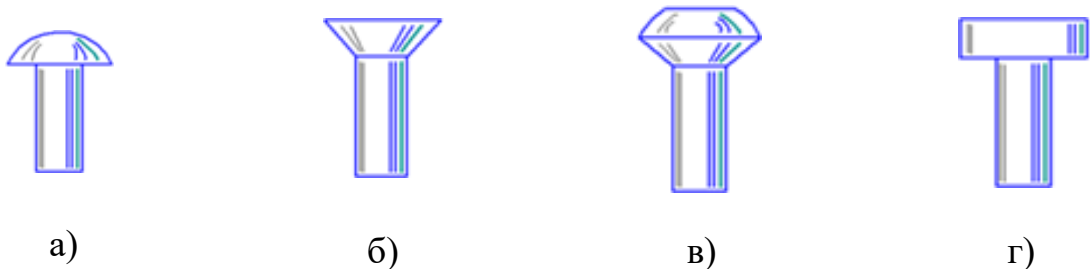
Види заклепок: а - напівкругла, б - потайна, в - напівпотайною, г - плоска
